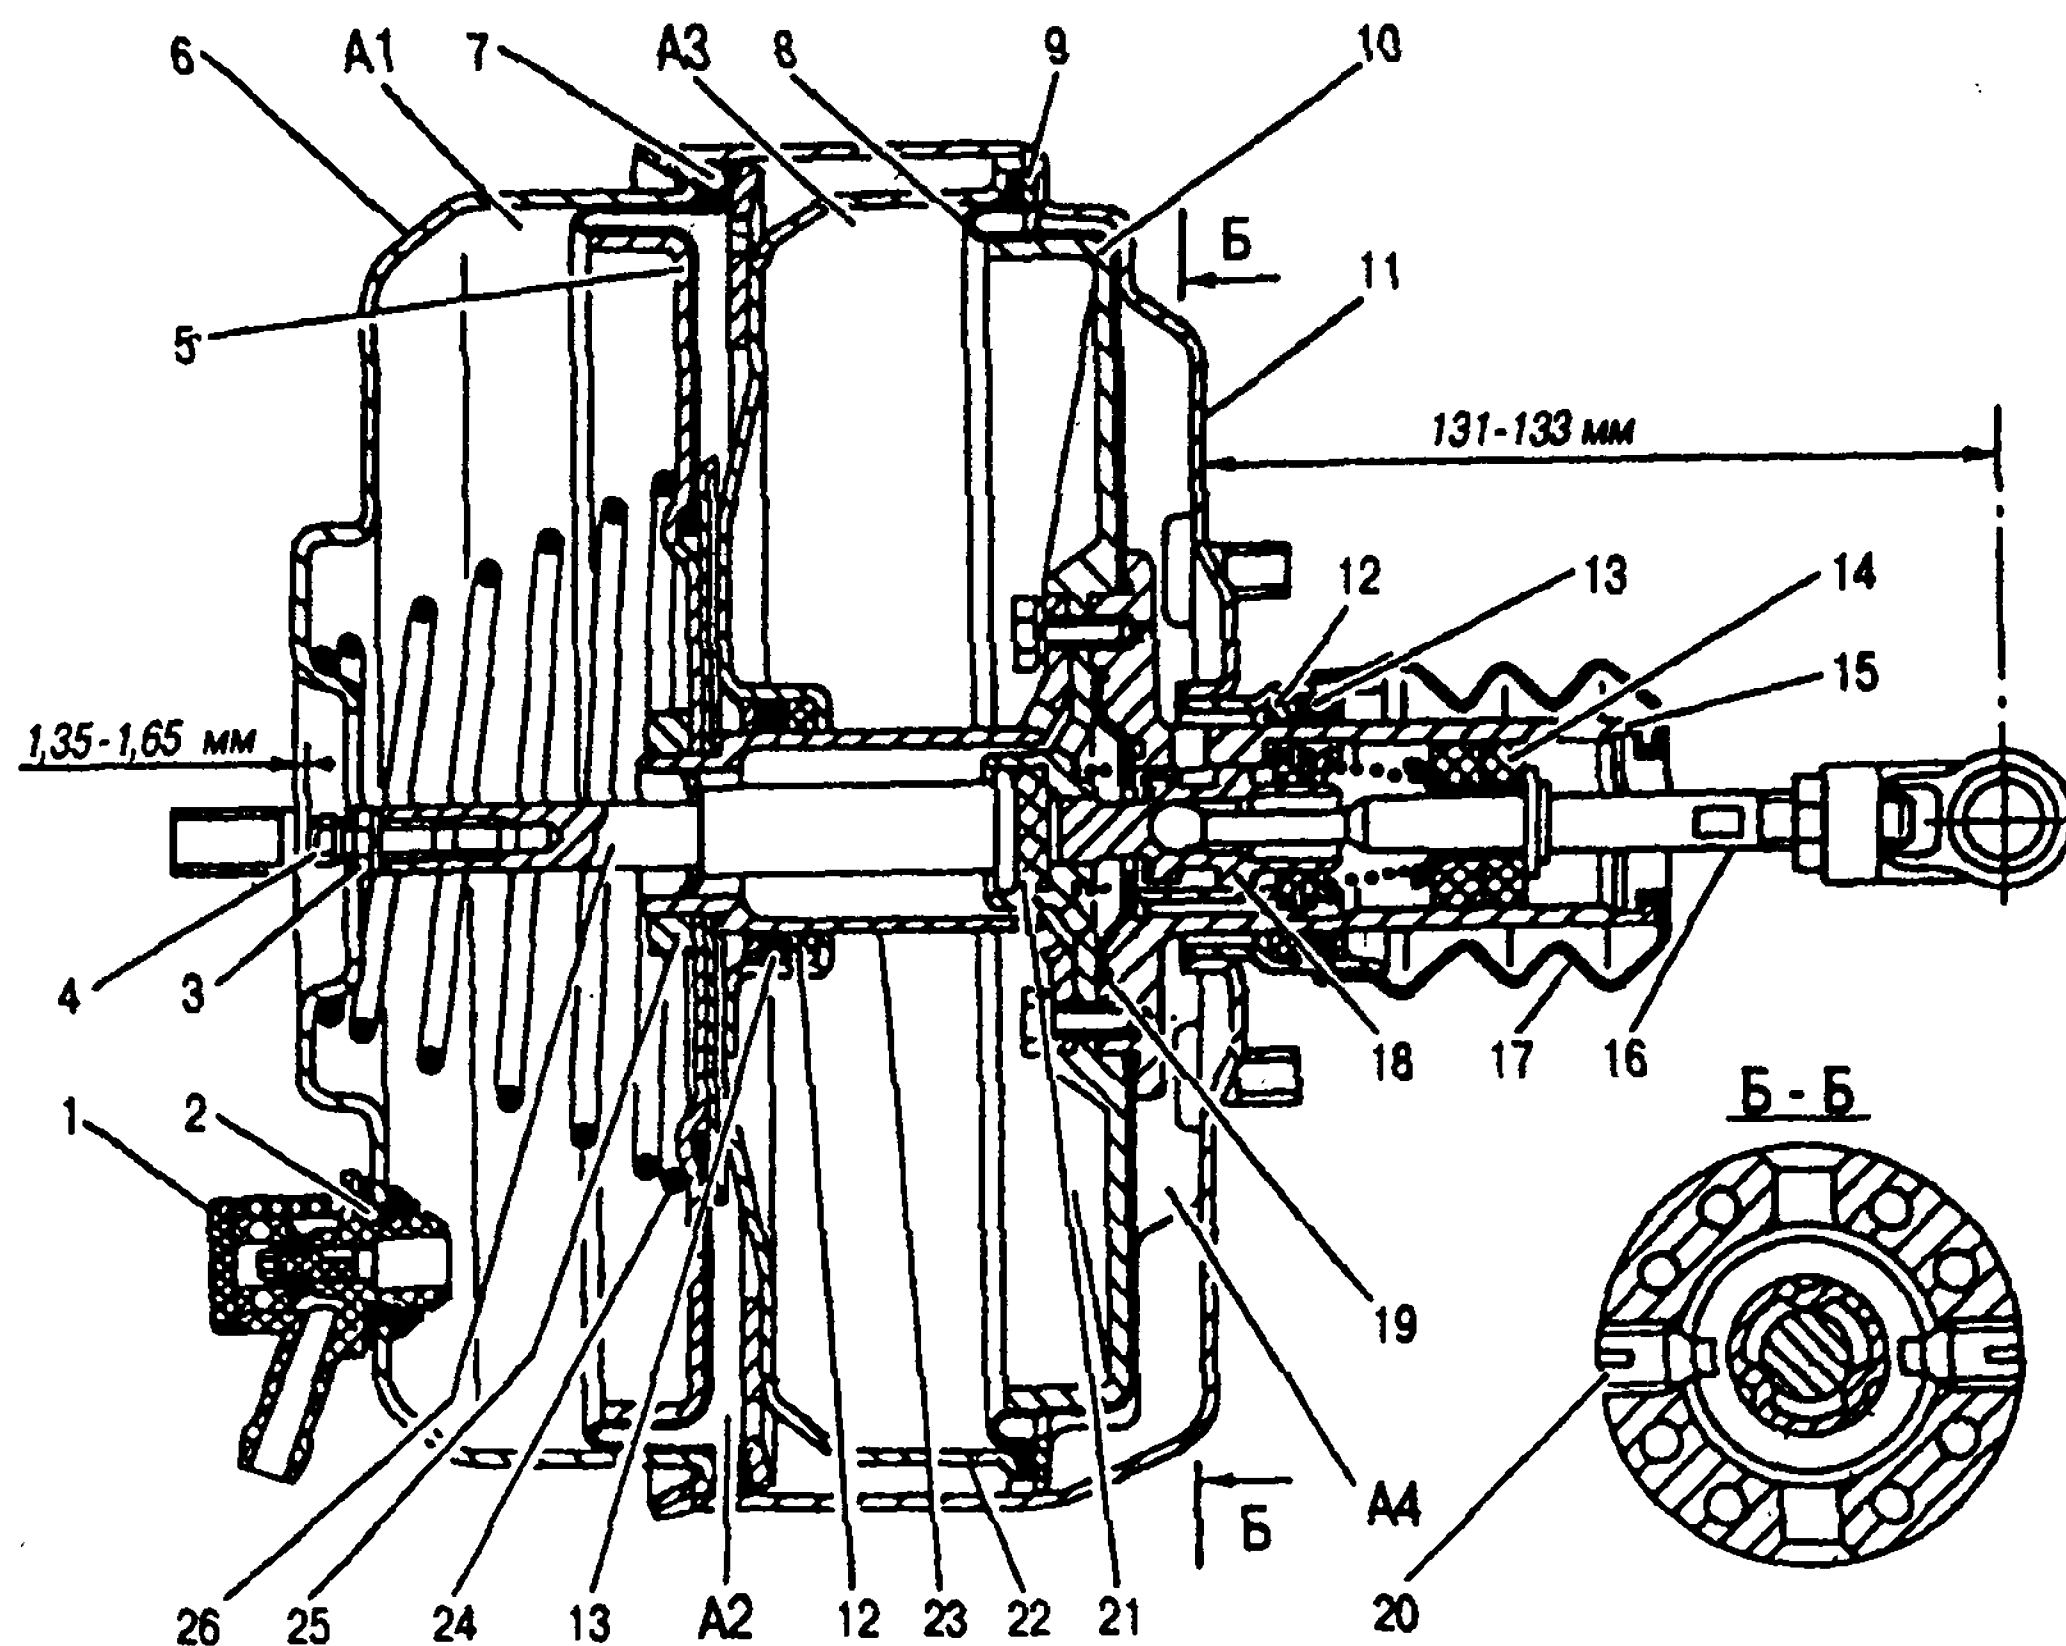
Вакуумный усилитель: 1 - обратный клапан; 2 - уплотнительная втулка; 3, 25 - гайки; 4 - регулировочный болт; 5, 10 - поршни; 6 - крышка корпуса; 7, 8 - диафрагмы; 9 - упорное кольцо; 11 - корпус усилителя; 12 - направляющее кольцо; 13 - уплотнительная манжета; 14 - фильтр; 15 - корпус клапанов; 16, 26 - толкатели; 17 - защитный чехол; 18 - поршень; 19 - диафрагма клапанов; 20 - винт; 21 - реактивная шайба; 22 - крышка упорная; 23 - соединитель поршней; 24 - пружина; А 1, А 2, А 3, А 4 - полости вакуумного усилителя
